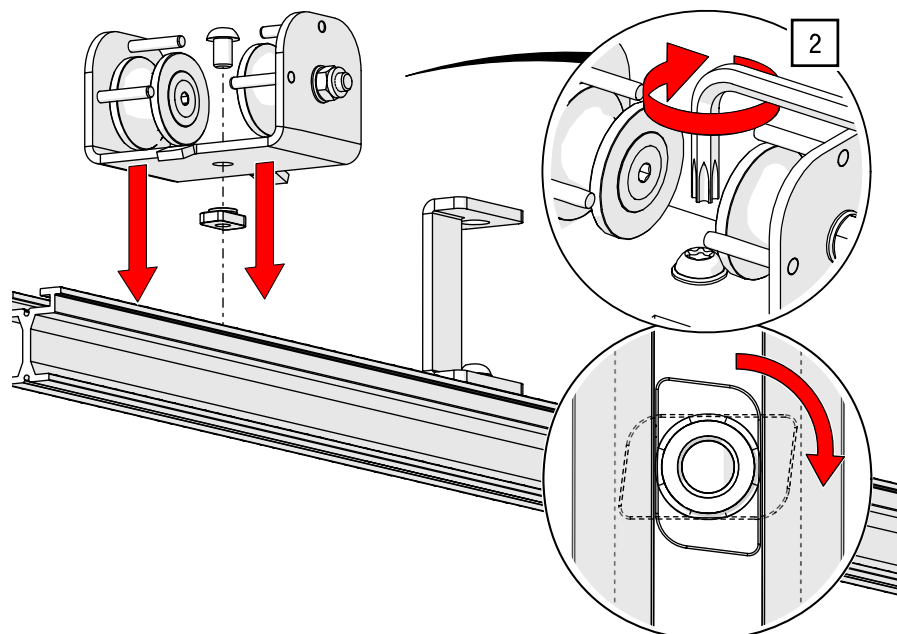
Doppelt obenliegende Seilführung – Umlenkrolle montieren
